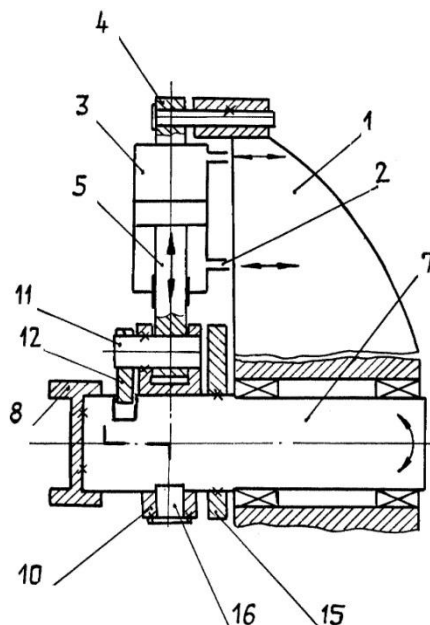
Поворотний механізм: 1 – корпус; 2 – шланги, для з'єднання; 3 – гідроциліндр; 4 – вісь мала; 5 – стійка; 7 – вал; 6 – кришка; 8 – перехідник; 9 – стопор; 10 – коромисло; 11 – вісь; 13 – підшипник; 12 – стійка.
